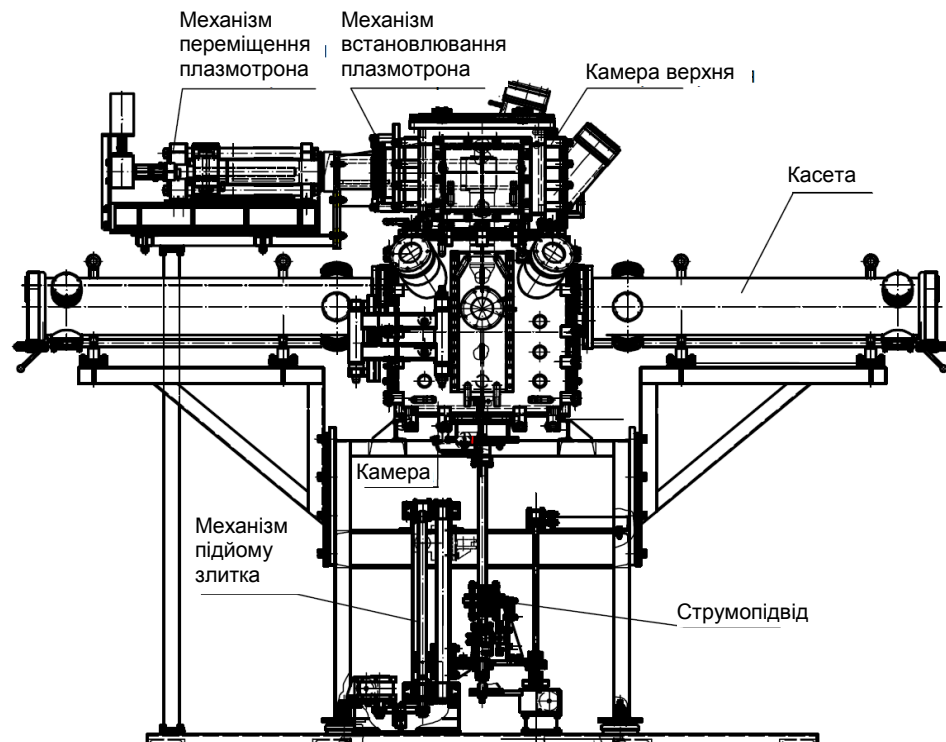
Принципова схема плазмово-індукційної установки УП-122М
